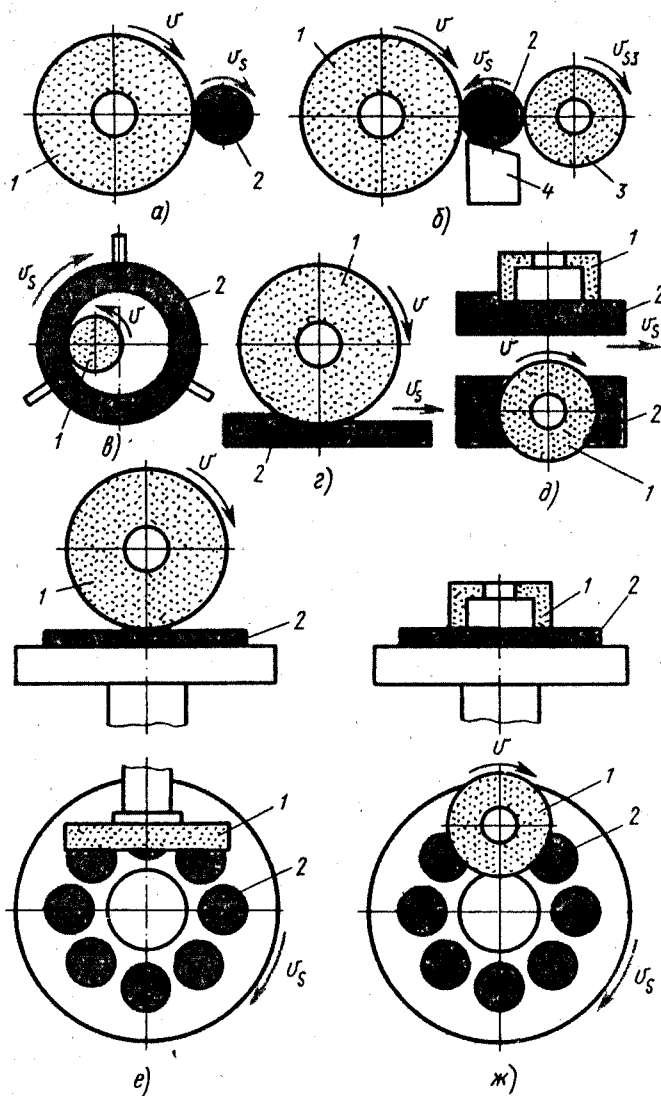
Схемы расположения круга и заготовки и направления движения подачи при шлифовании периферией круга (а, б, в, г, е) и торцом круга (д, ж):
